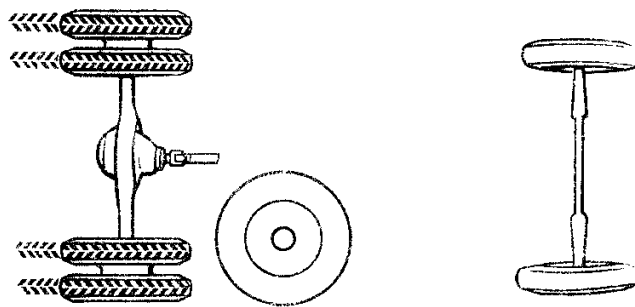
Установка шин с грунтозацепами типа "елка" на колеса
